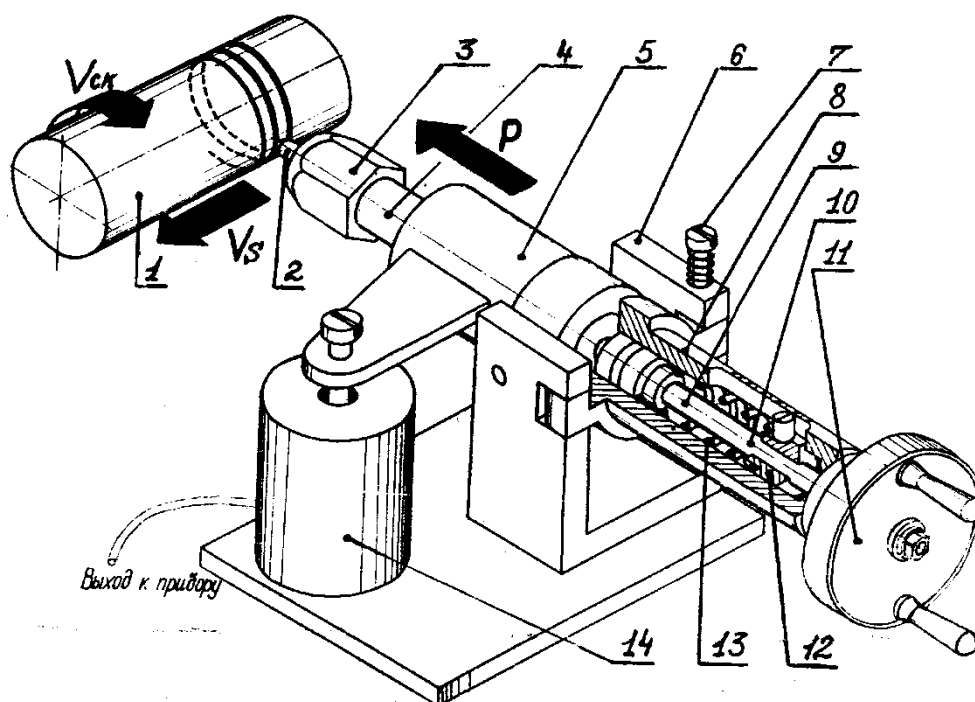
Схема работы моделирующей установки. 1-индентор; 2-контртело; 3-гайка; 4-шток; 5-корпус штока; 6-стойка; 7-зажим; 8-корпус зажимного устройства; 9-толкатель; 10-вал; 11-диск; 12-ползун; 13- пружина; 14-датчик давления;
